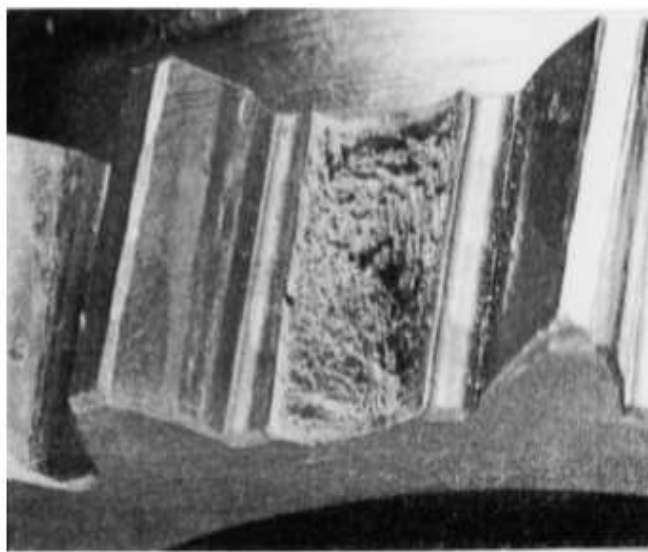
Злам зуба прямозубого колеса при перевантаженні
